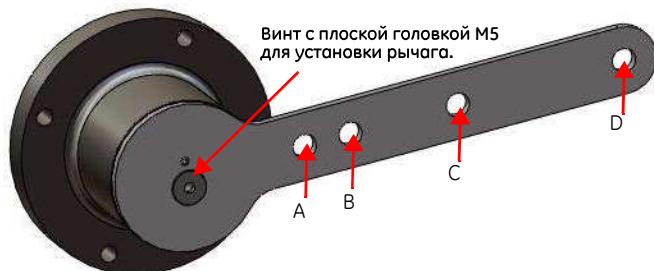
Держатель магнита и стандартный рычаг для поршневых клапанов
